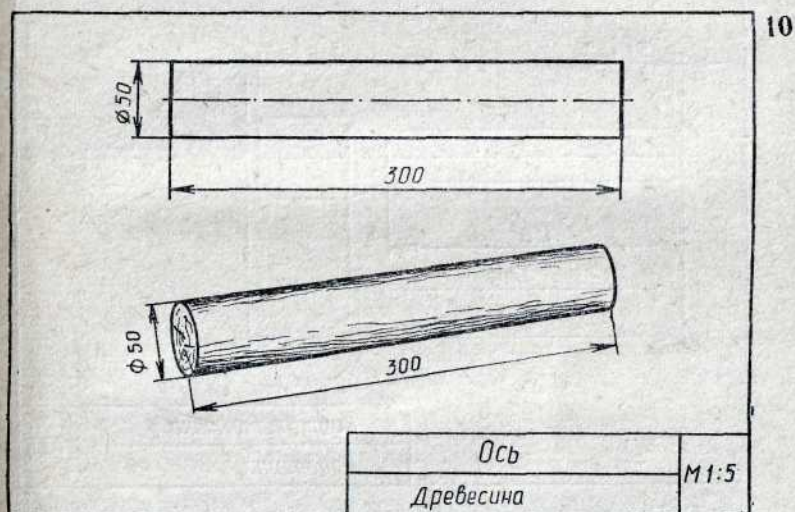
Технический рисунок и чертеж простой цилиндрической детали.
